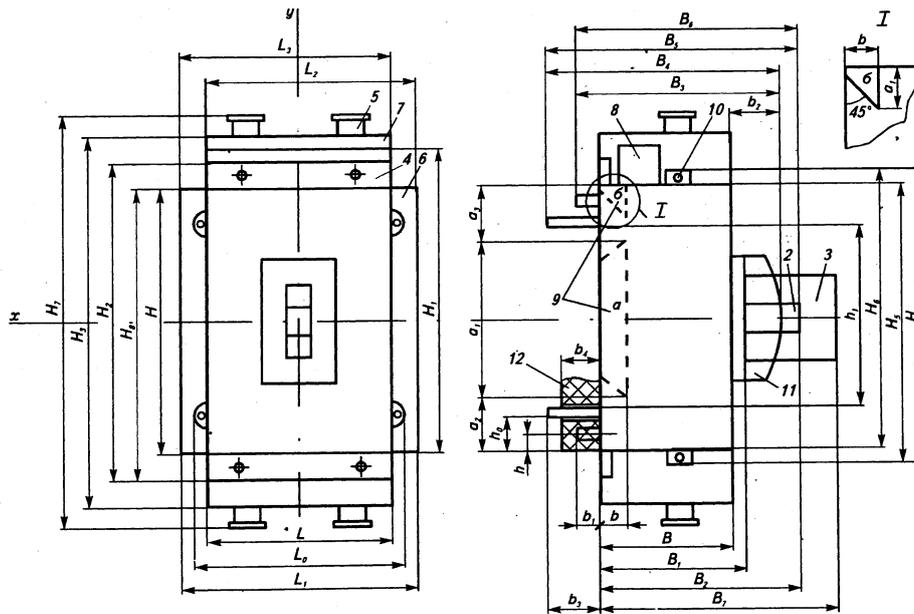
Габаритный чертеж выключателей стационарного исполнения с ручным приводом
